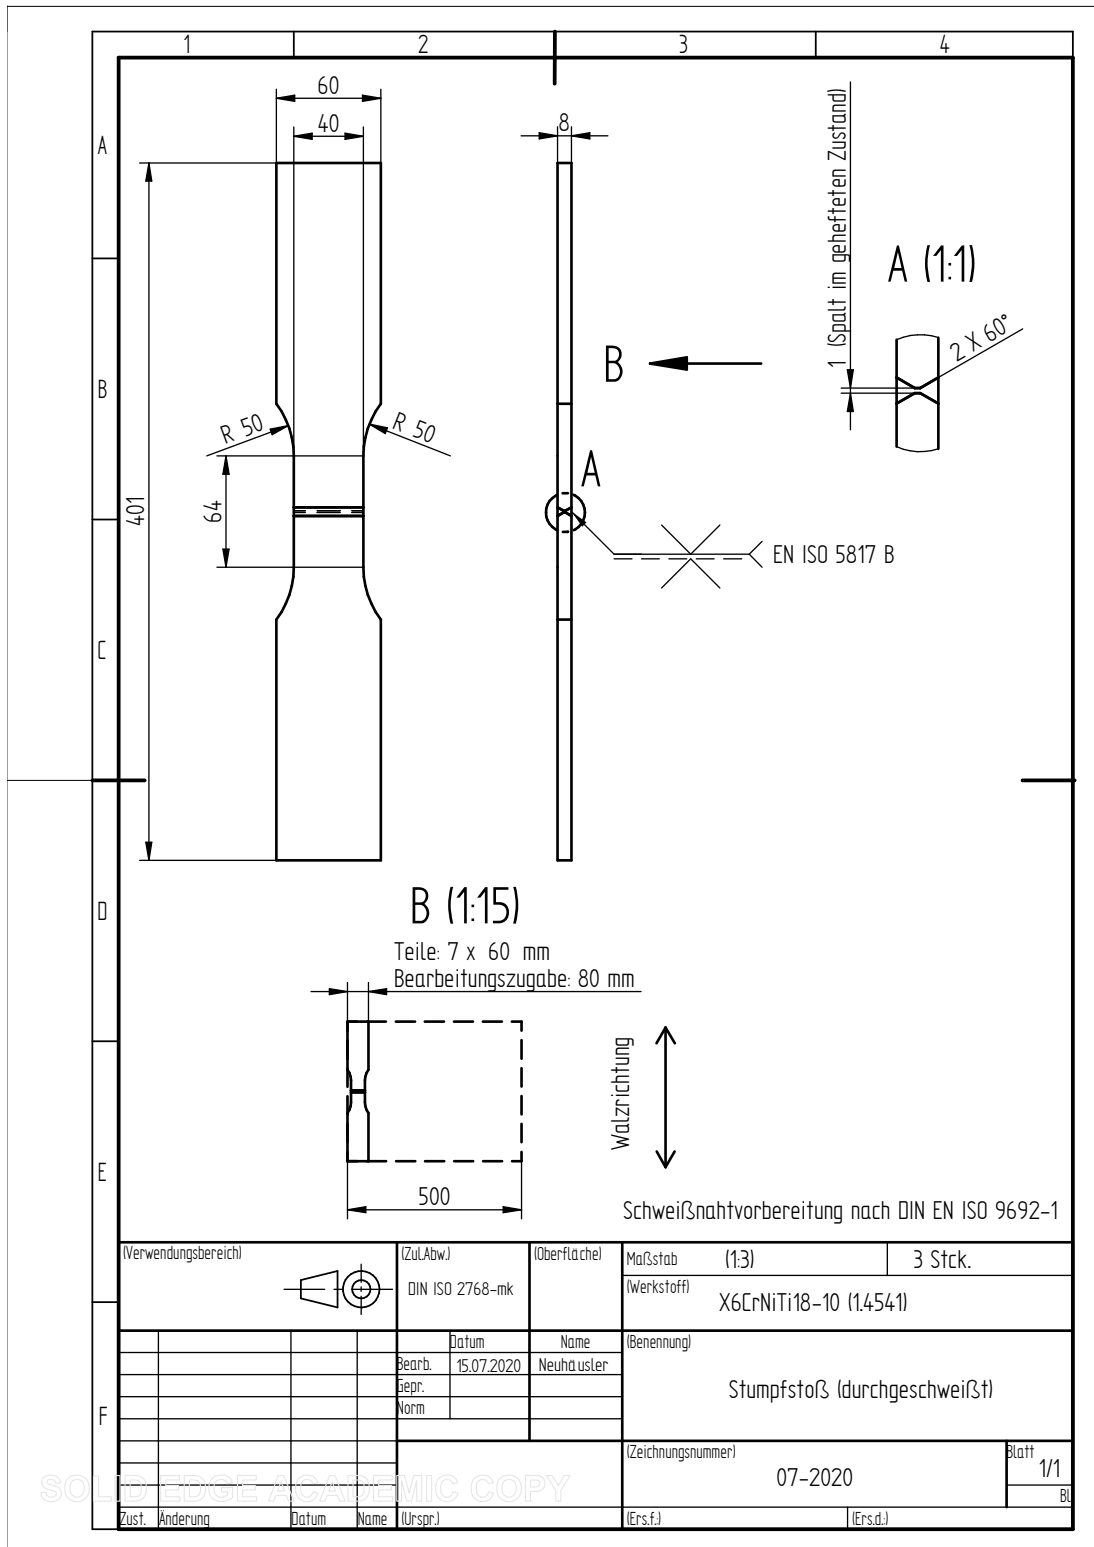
Fertigungszeichnung für die Stumpfstoßproben aus 1.4541 [67].
